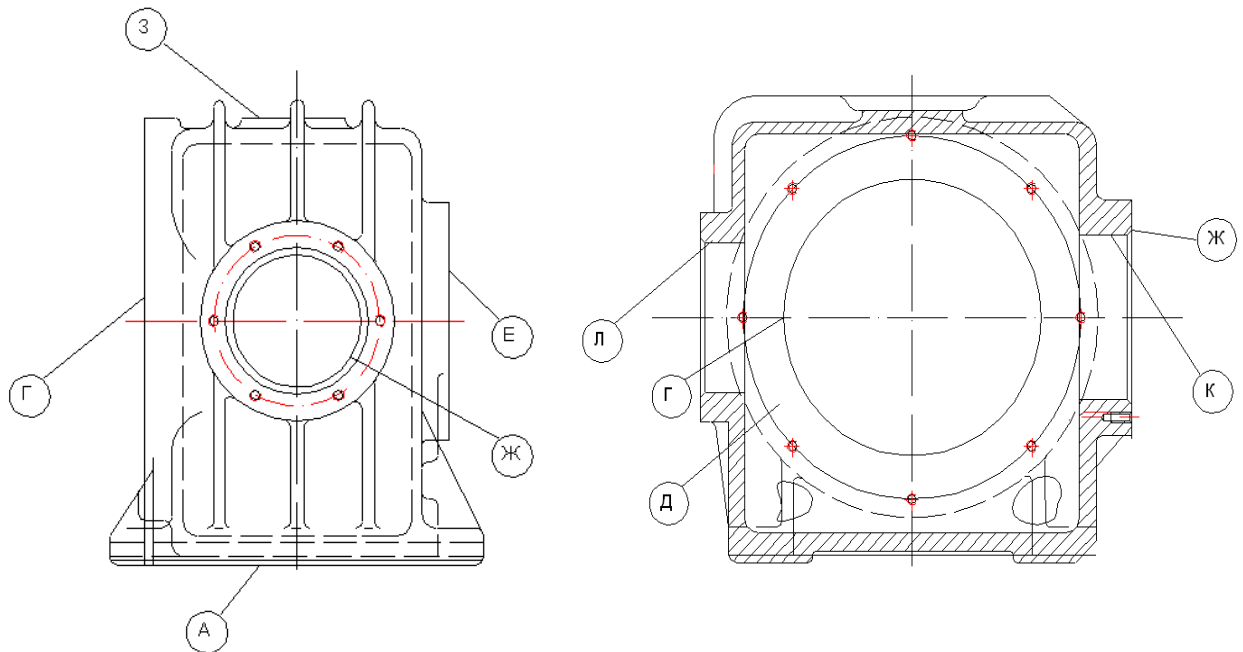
Ескіз деталі «Корпус редуктора КСБВ-11.021.444» з поверхнями які підлягають обробці
